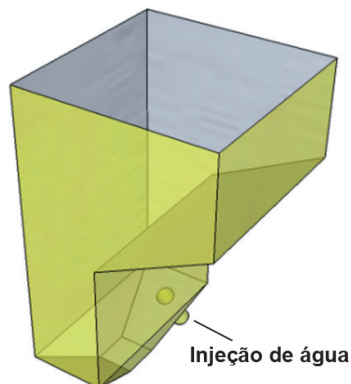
C. Cortes das chapas, dobras e montagem e aspecto final do separador de cerejas.
